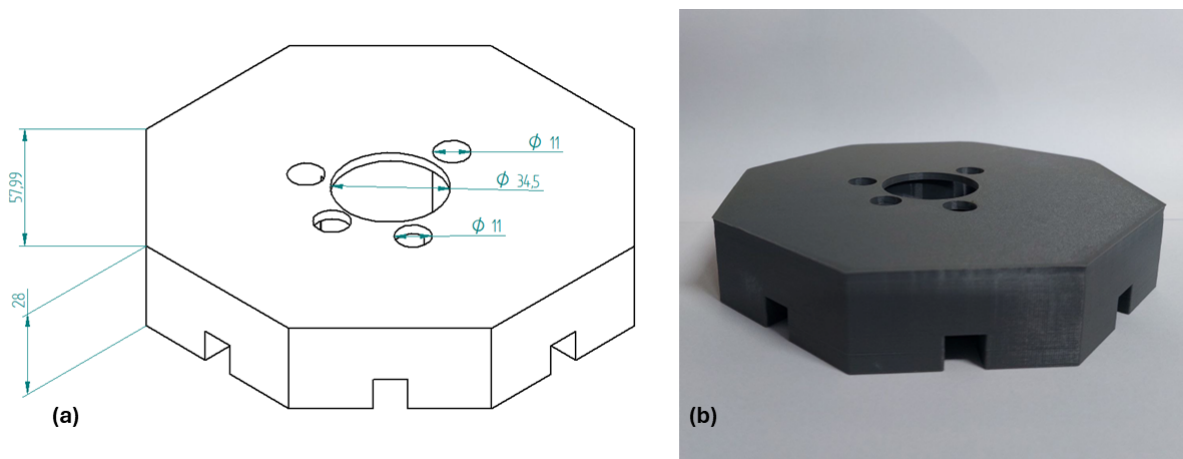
Vista isométrica da peça central: (a) Desenho técnico (b) Peça impressa.
